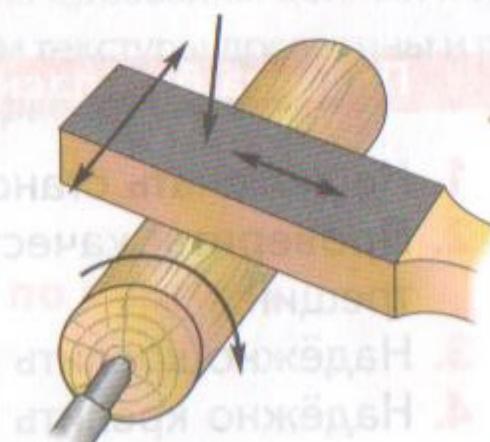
Шлифование вращающейся цилиндрической детали колодкой
